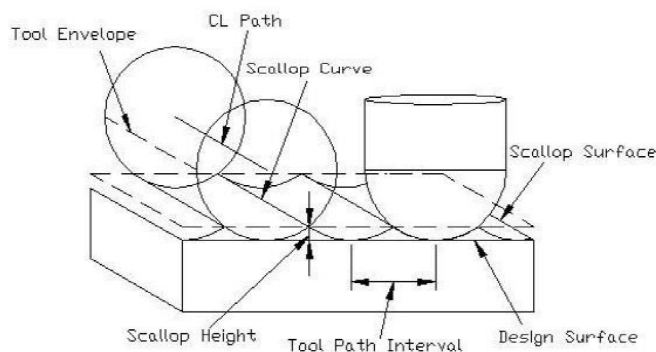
Геометричні елементи обробленої поверхні [38]
